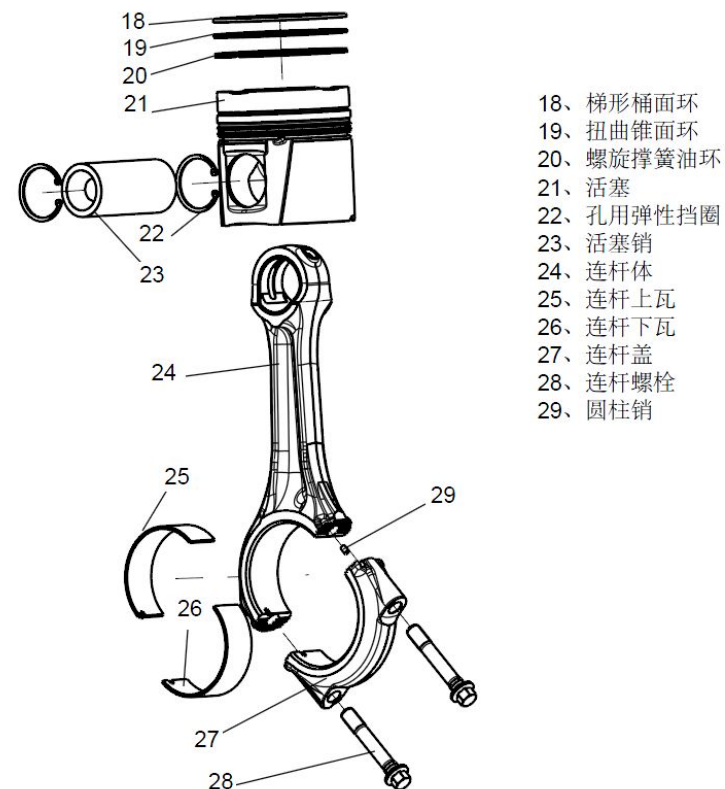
Схема разборки шатуна поршня 16М33.
